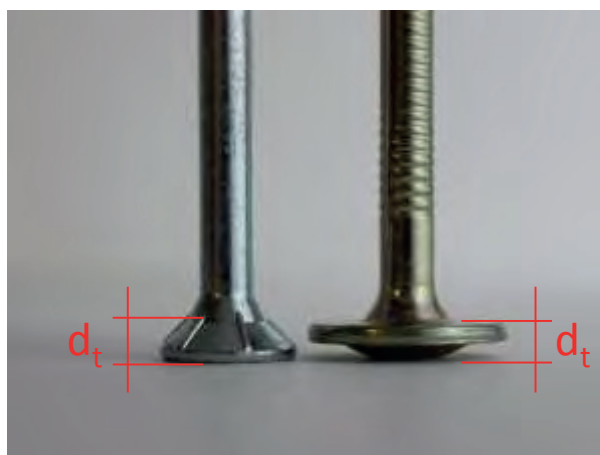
Schraubenkopfhöhe  $d_i$  einer Senkkopfschraube (li) und einer Tellerkopfschraube (re) zur Auswertung des Schraubenkopfdurchziehparameters  $f_{head,w}$
